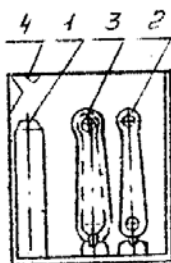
Схема многоручьевого штампа для штамповки поковки шатуна:
